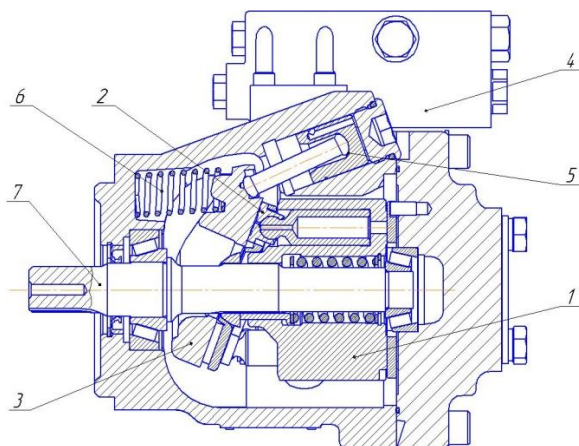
Регульований аксіальний роторнопоршневий насос типу PVC 1.63: 1 – блок циліндрів; 2 – п'ята; 3 – похилий диск; 4 – LS- регулятор типу PVN; 5 – гідроциліндр керування; 6 – пружина віджиму люльки; 7 – приводний вал
